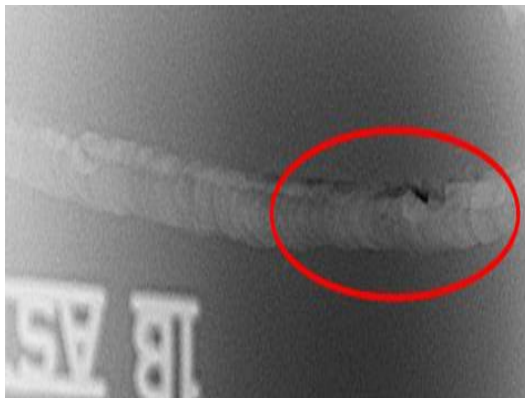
Falta de fusión en el bisel de la soldadura
